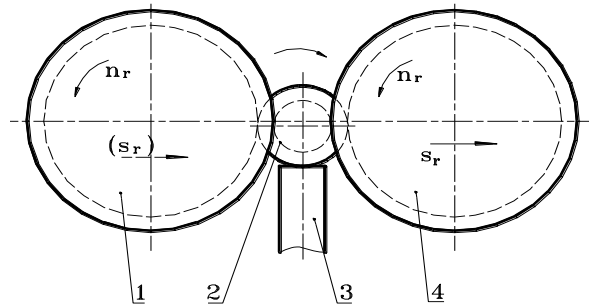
Principe de formage avec deux roues et avance radiale sur des machines spécialisées
